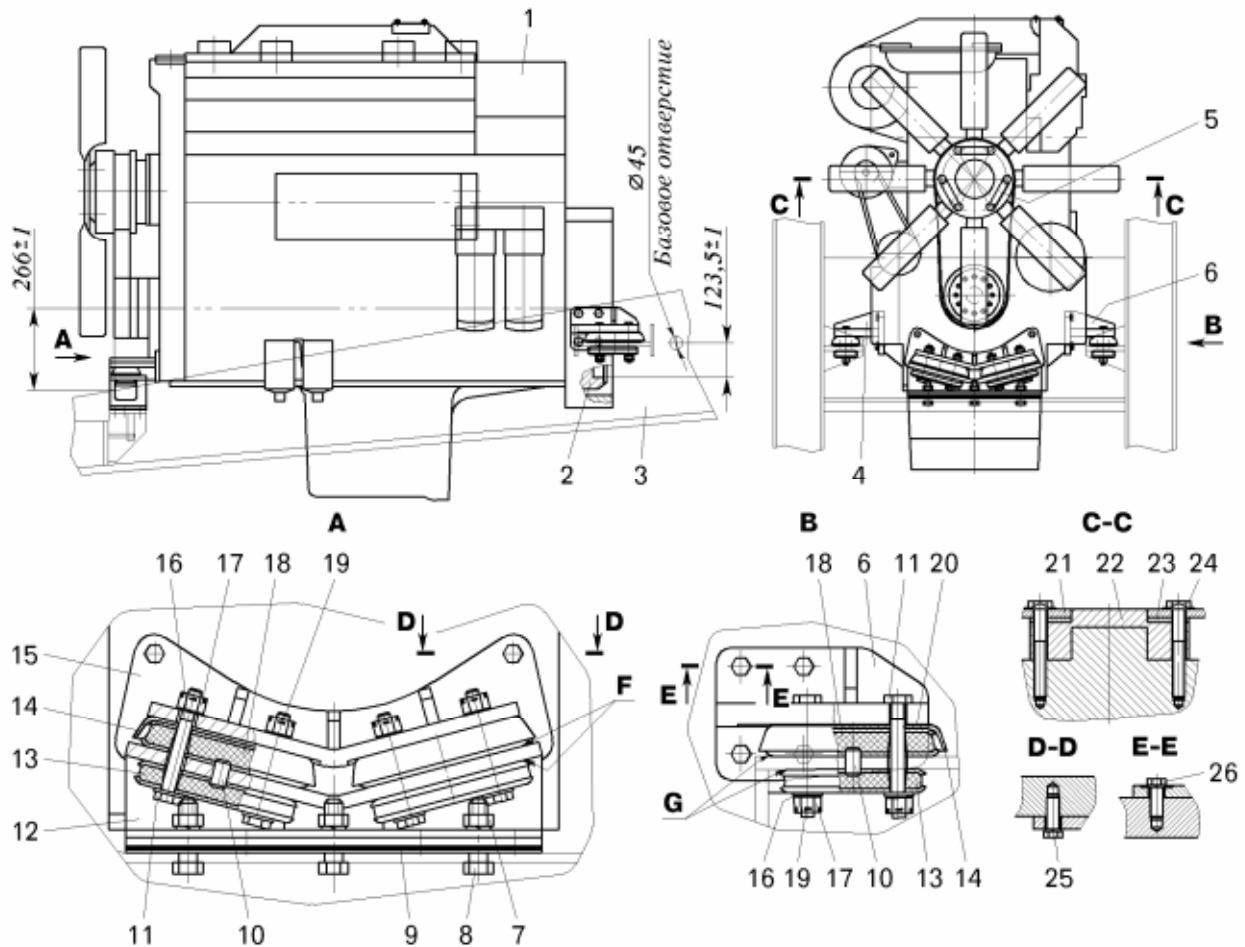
Установка двигателя самосвала БелАЗ-7555Е:
